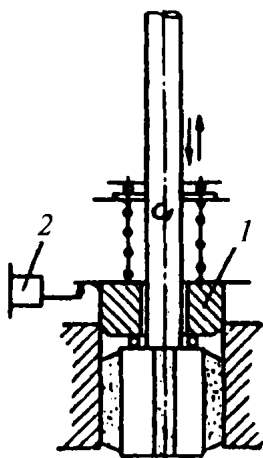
Схема измерительного устройства для хонинговального станка
